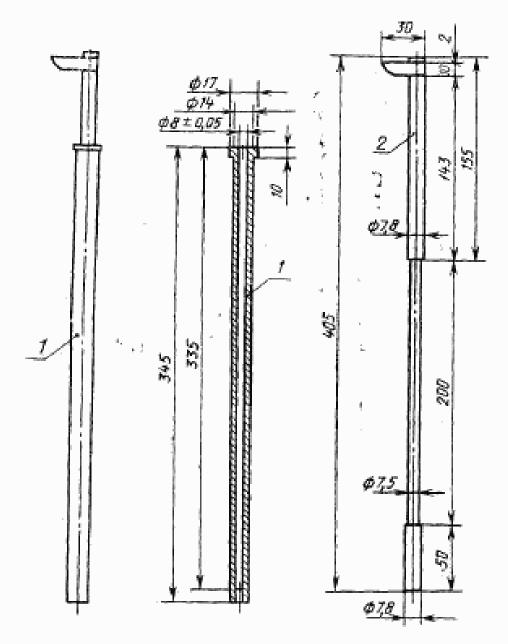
Приспособление для выталкивания угольного стержия — пресс
